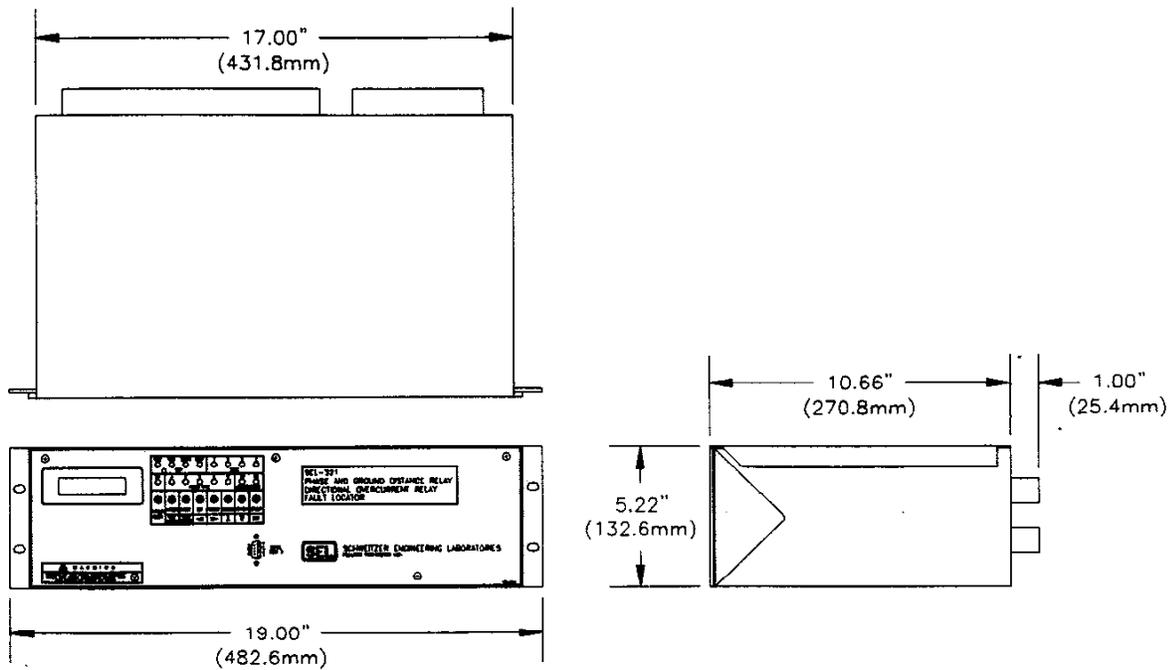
Relais SEL-321, Vues de face avant et arrière, montage horizontal, (version 1 carte I/O)
